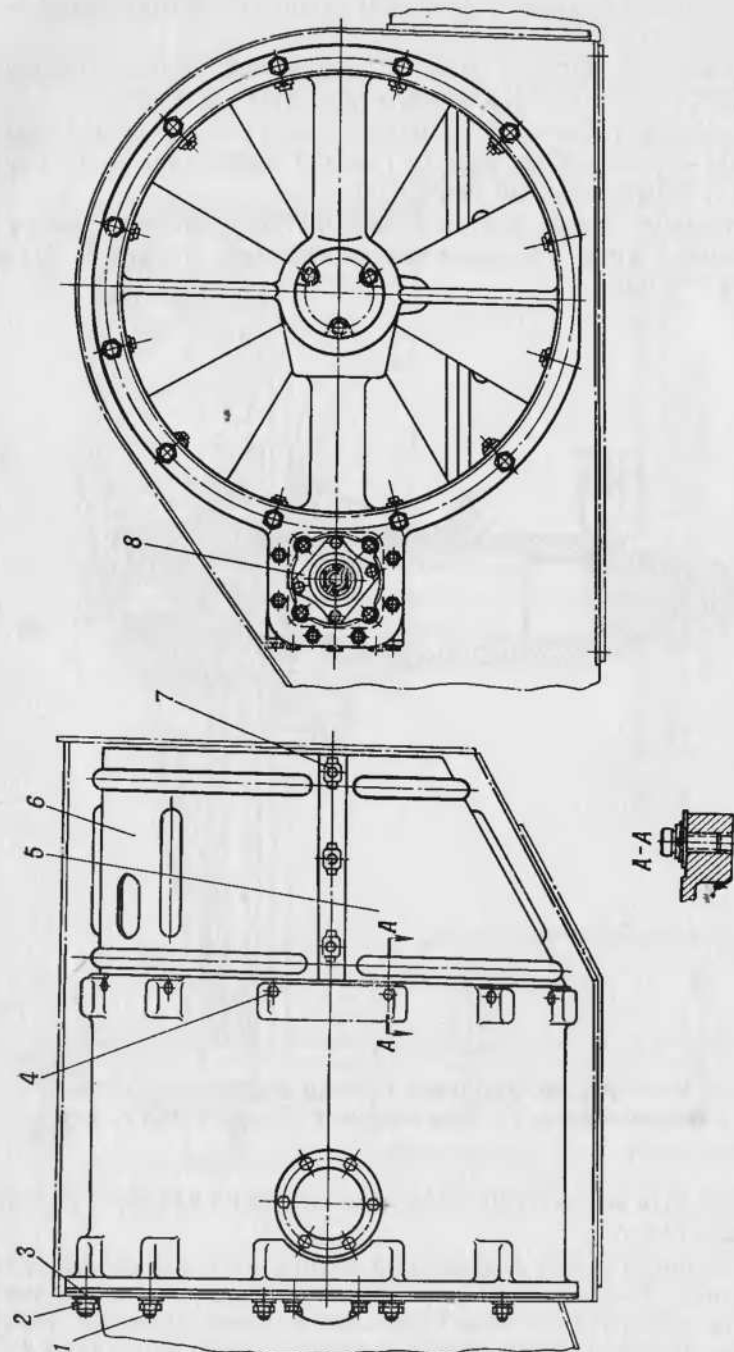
Установка водометного движителя: 1 — шпилька; 2 — гайка; 3 — уплотнительная прокладка; 4 и 7 — болты; 5 — нижняя часть диффузора; 6 — верхняя часть диффузора; 8 — фланец
